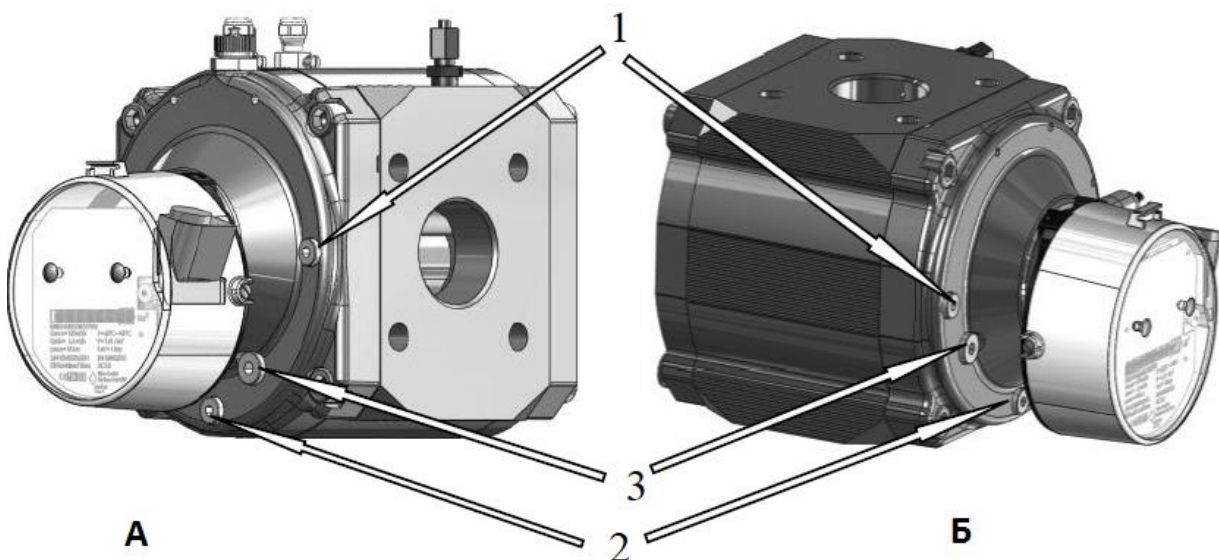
Схема розміщення отворів для заливки масла на корпусі лічильника
